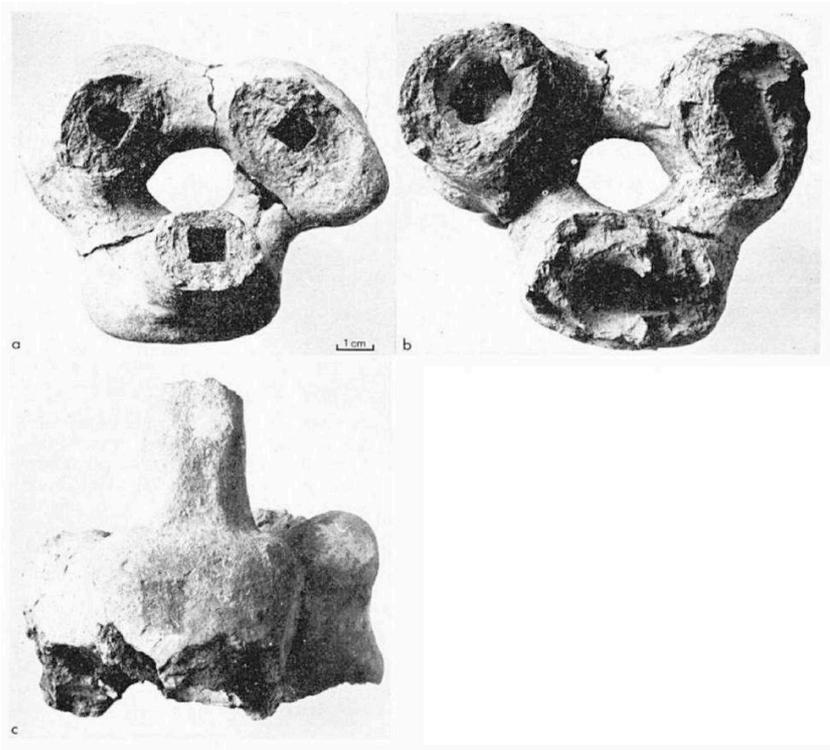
Fragment de moule triple d’anneaux passe-guides (inv. P. 78-910, 911, 912) : a) vue de dessus, b) vue de dessous, c) vue de profil (h. conservée 8,5 cm).
